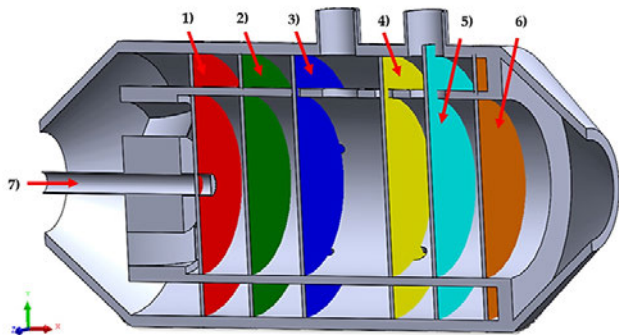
Vista de los planos yz y origen de la cámara de combustión: (1) plano a; (2) plano b; (3) plano c; (4) plano d; (5) plano e; (6) plano f; (7) origen.
